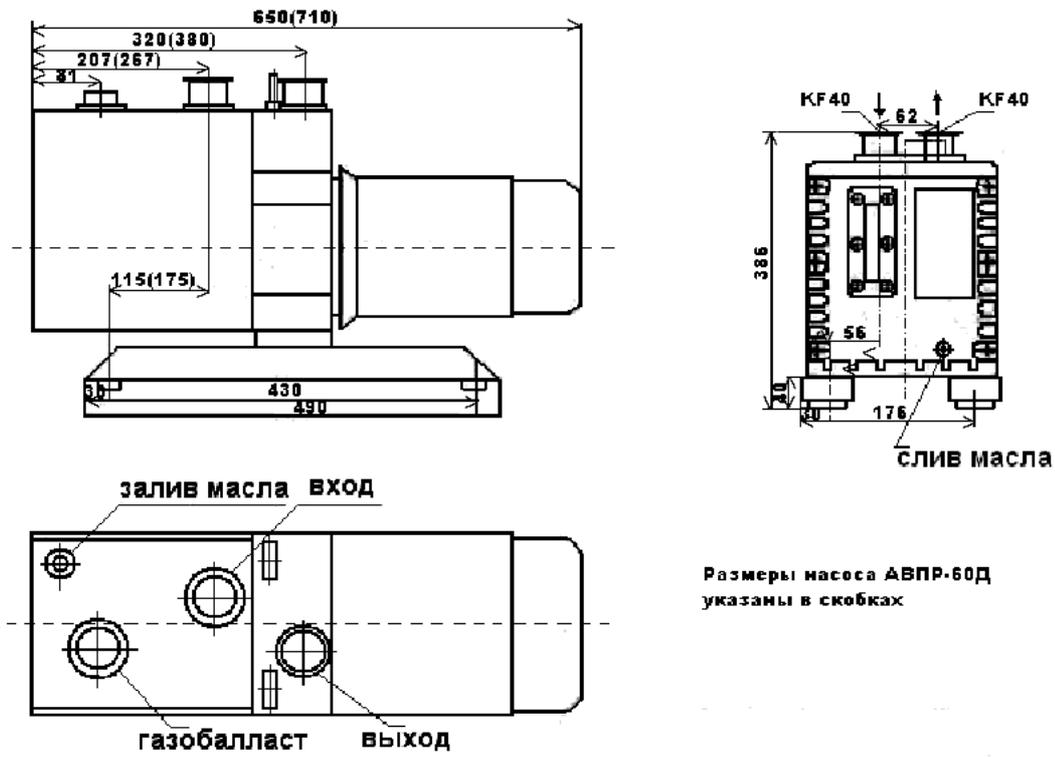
Габаритный чертеж АВПР-30Д, АВПР-60Д
